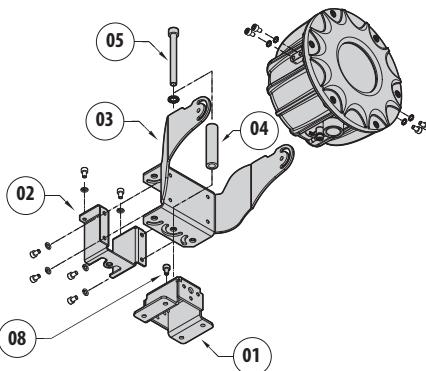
Fixation sur parapet avec entrée des câbles dirigée vers le bas.
